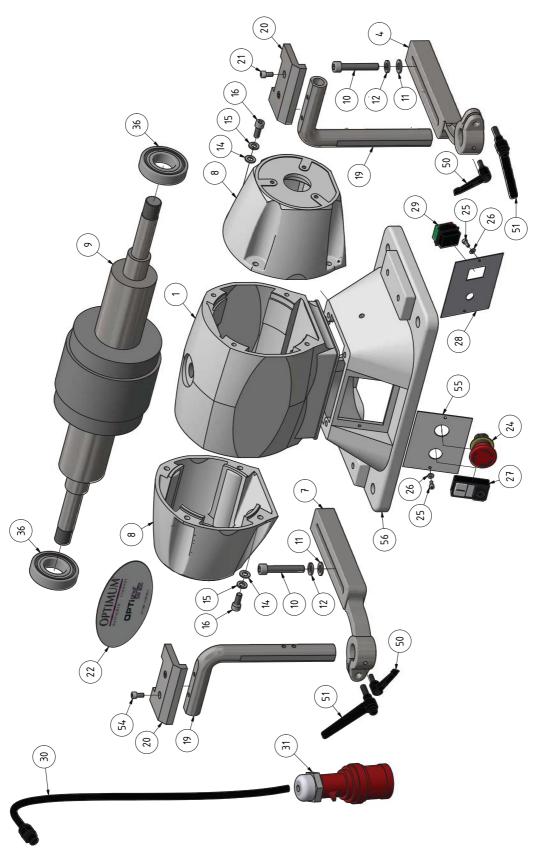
Ersatzteilzeichnung 2 von 2 - Drawing spare parts 2 of 2
